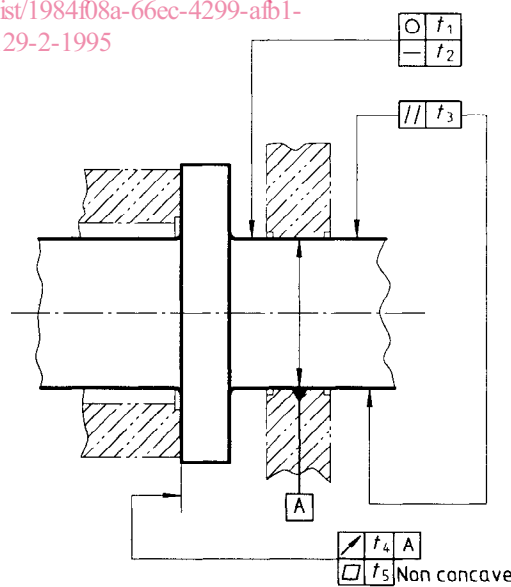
Arbres à collerette ou collet de butée pour palier radial, capable de supporter une charge d'un seul côté — D
